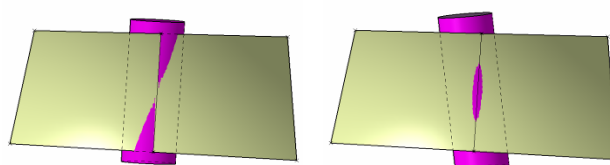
Interférences outil – surface à usiner, en usinage par le flanc
